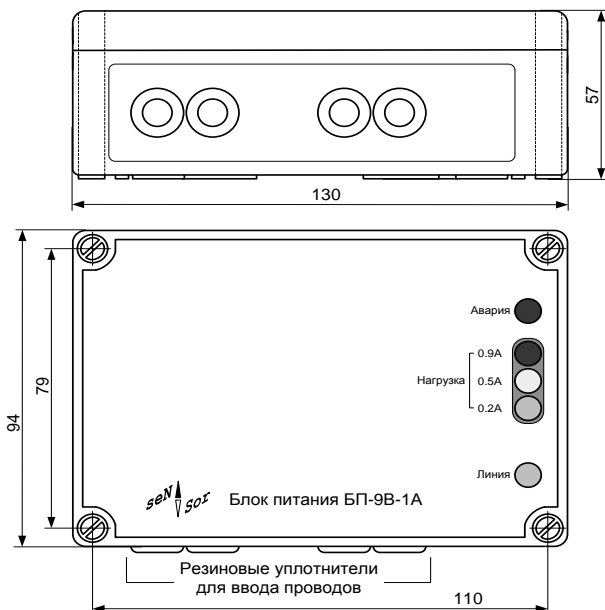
Внешний вид, габаритные и установочные размеры изделия обычного исполнения
